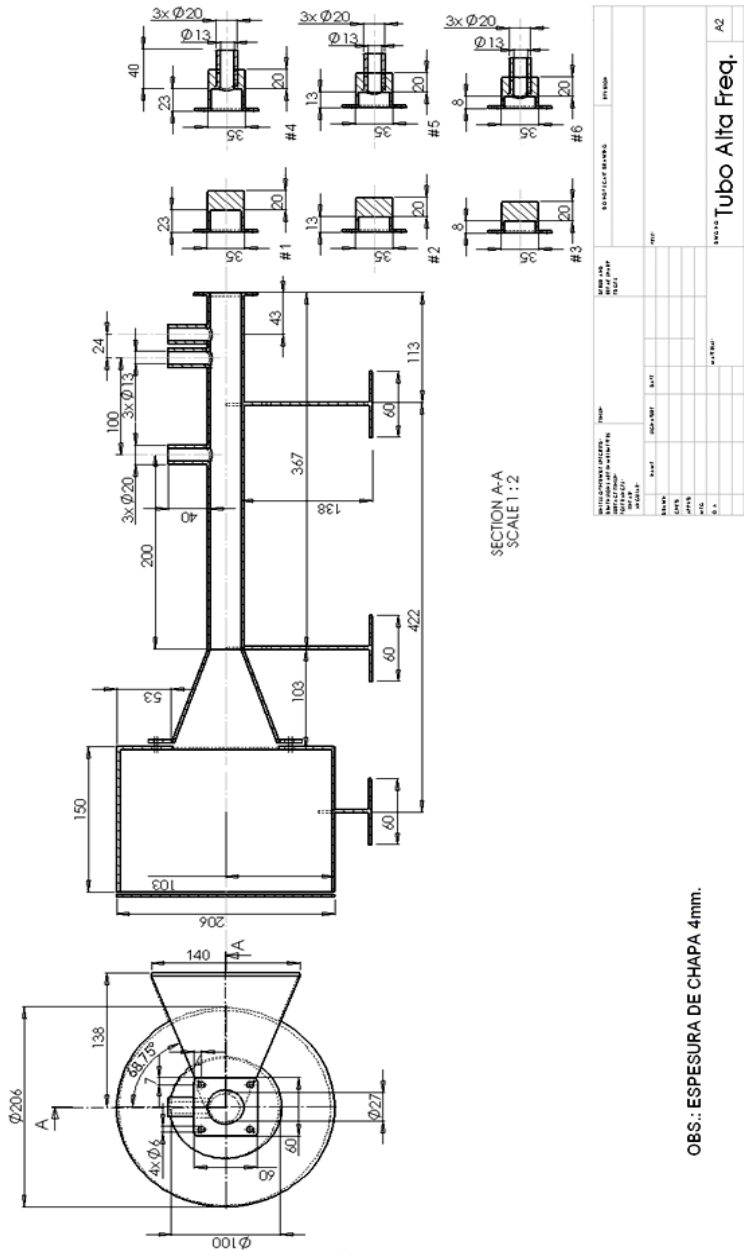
Dimensões em mm do tubo de impedância fabricado.
